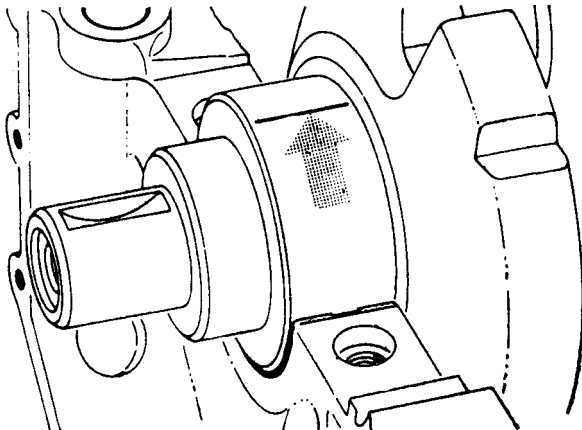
Установка пластикового калибра на шейку коленвала для измерения зазора в подшипнике.
